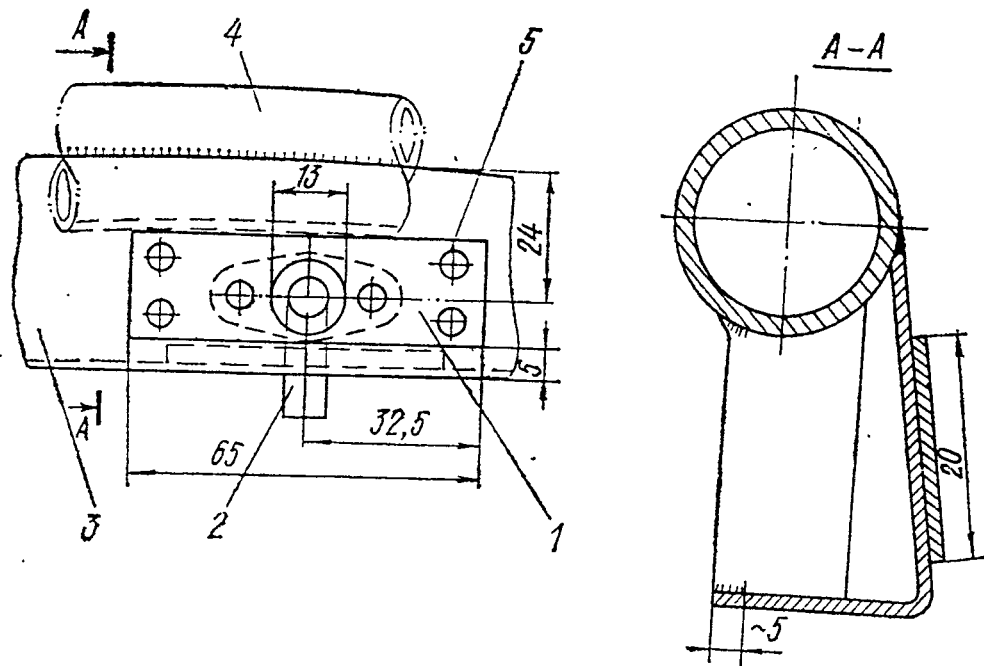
Эскиз 3 ремонта каркаса спинки пассажирского кресла:
